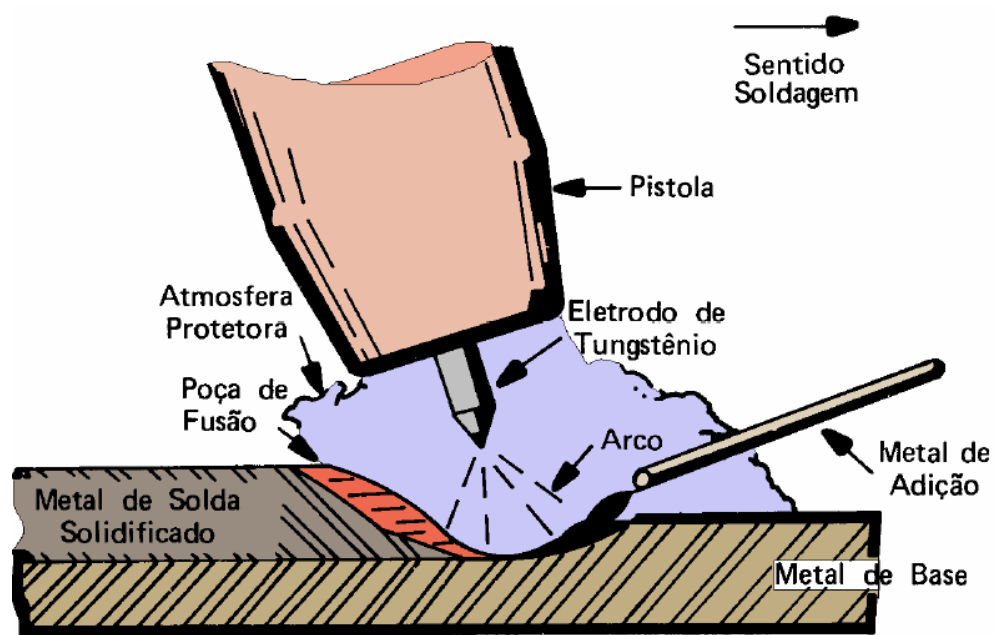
Soldagem TIG (detalhe) (MODENESI, 2006).
